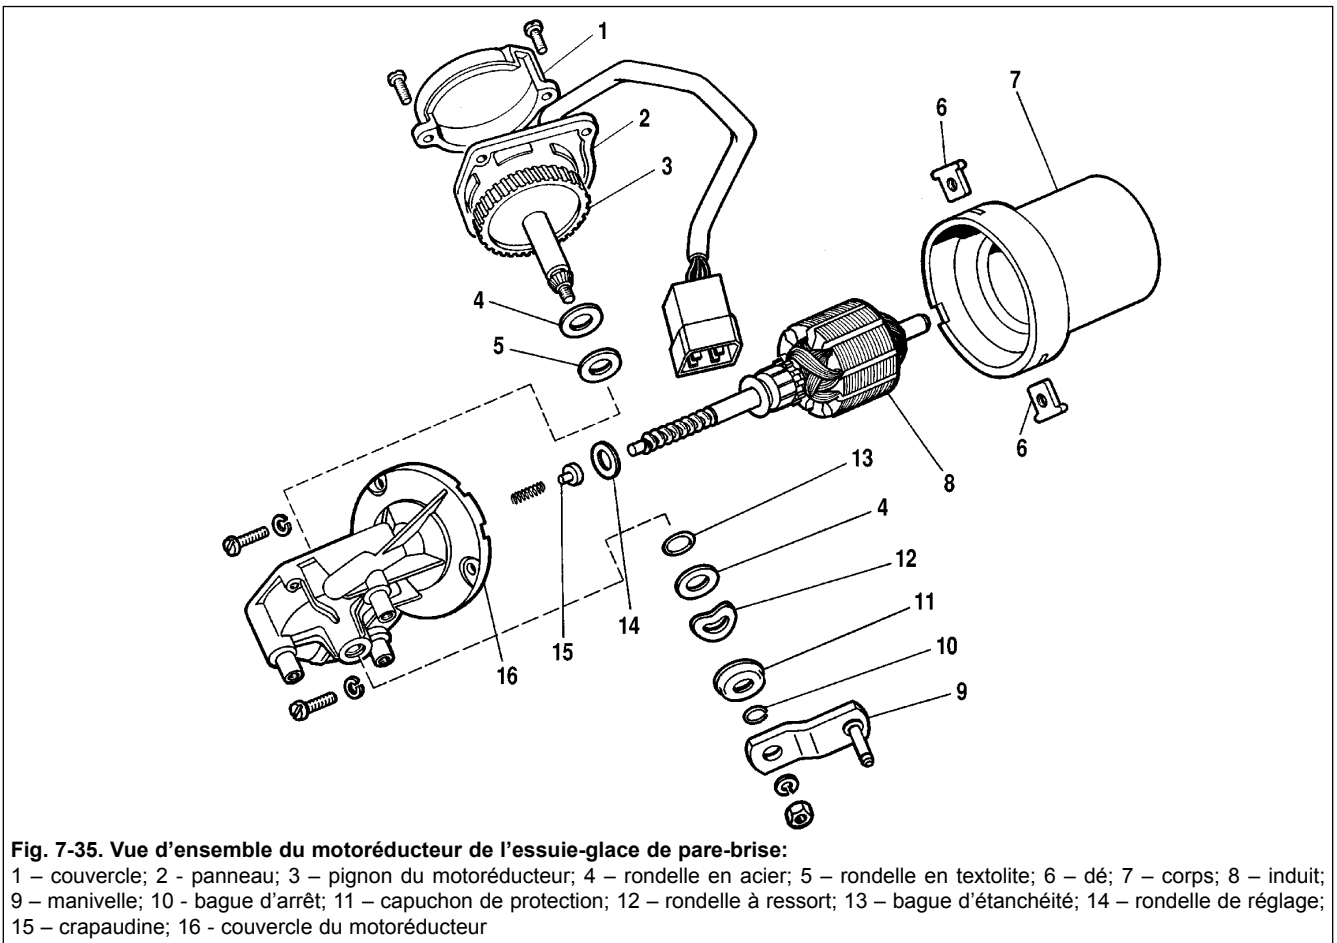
Vue d'ensemble du motoréducteur de l'essuie-glace de pare-brise:
